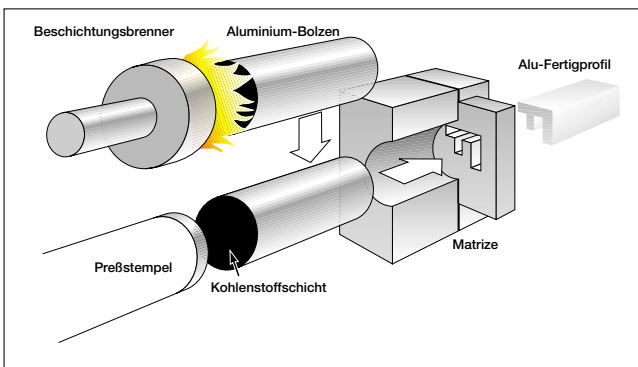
Bolzenbeschichtung beim Aluminium-Strangpressen
